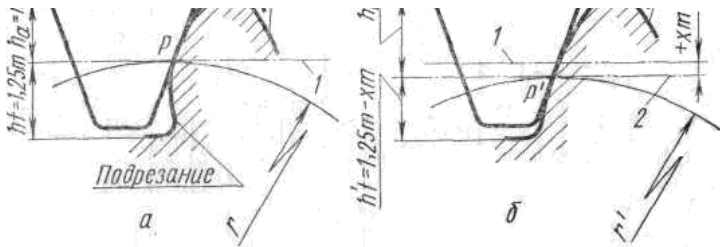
Смещение зуборезного инструмента при корректировании зубчатых колес
